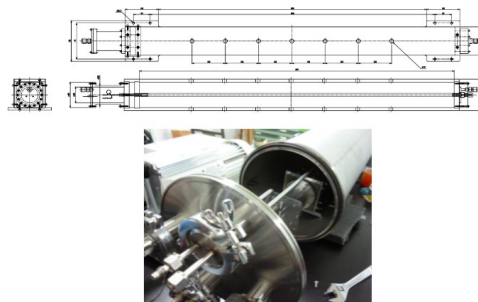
Одноканальный прототип строу: (наверху) чертеж прототипа; (внизу) общий вид стенда
